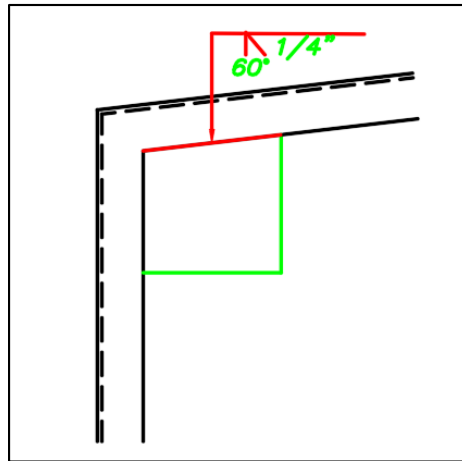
SIMBOLOGÍA DE JUNTA SOLDADA ENTRE BRIDA SUPERIOR Y CARTELA
